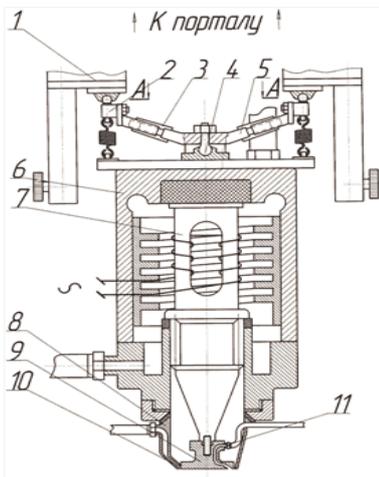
Ультразвуковое устройство для поверхностной обработки природного и искусственного камня, содержащее динамический гаситель колебаний
